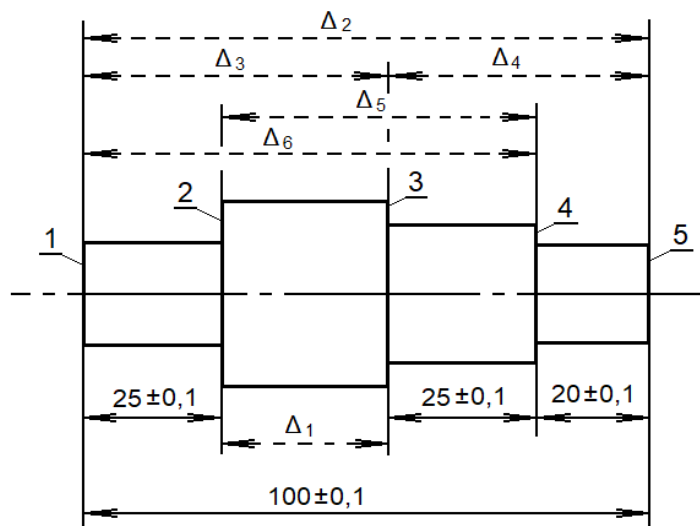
Эскиз детали с полным набором замыкающих звеньев размерной цепи
